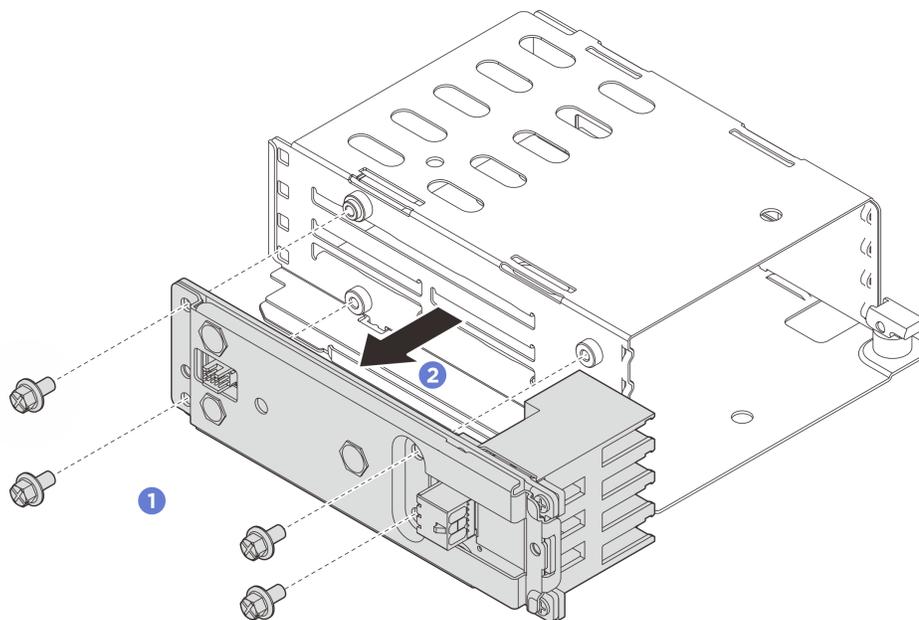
Entfernen der Rückwandplattenbaugruppe
